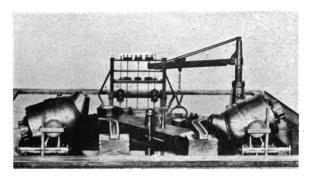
Appareil Bessemer pour la fabrication de l'acier (V. N° 7813)
